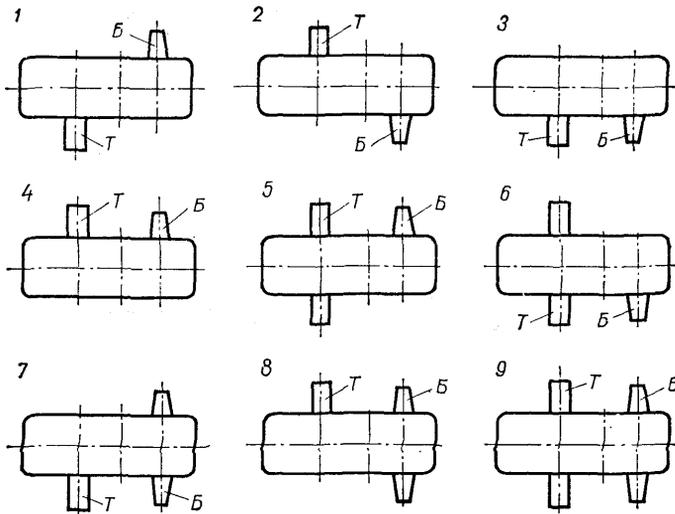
Схемы сборок (1—9) редукторов РМ:
